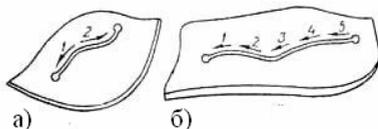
Схема заварки коротких (а) и длинных (б) трещин
